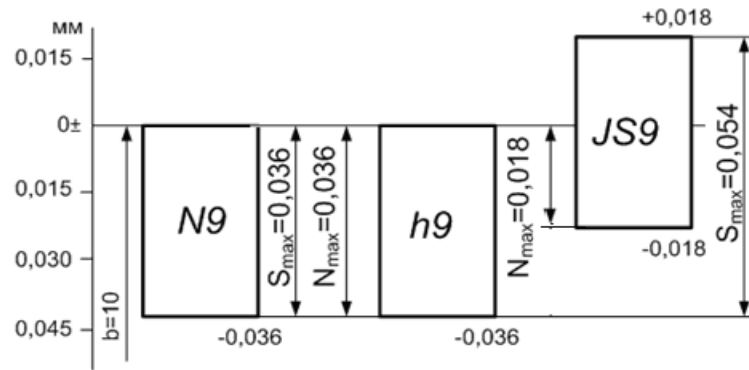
Схема полів допусків шпонкового з'єднання
